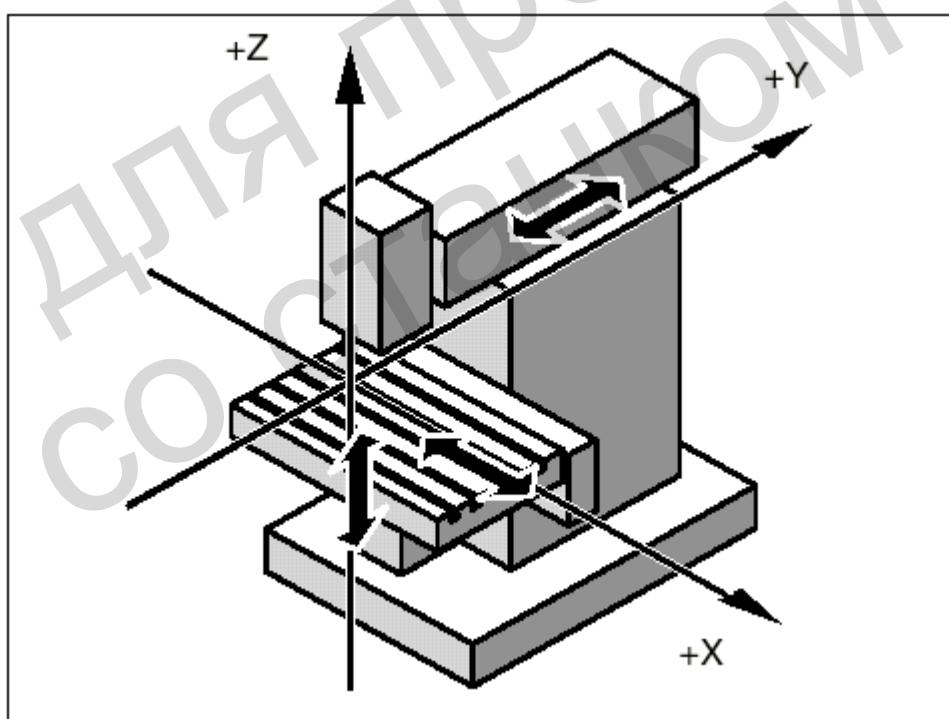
Координаты/оси станка на примере фрезерного станка
